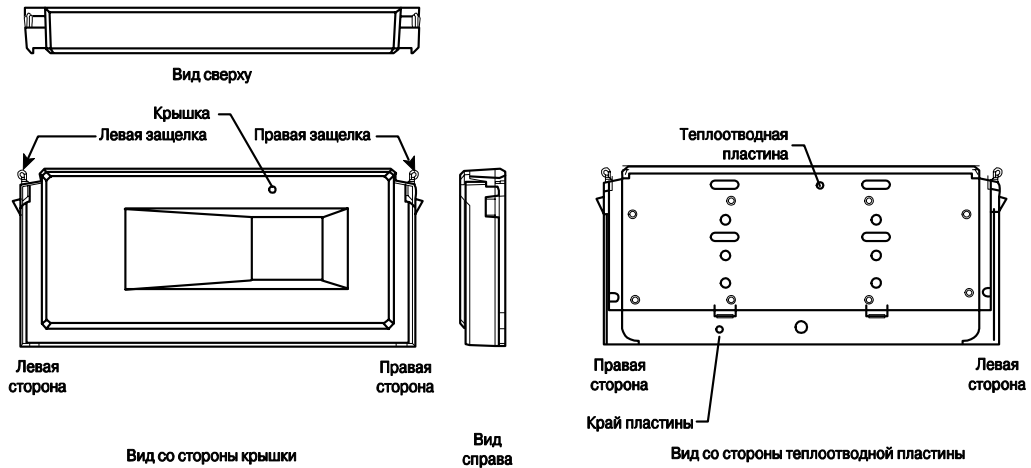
Детали корпуса SEC для процессора Pentium II
